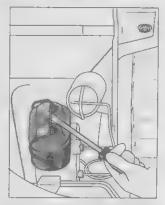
13. Снятие с помощью отвертки крышки металлического главного цилиндра
